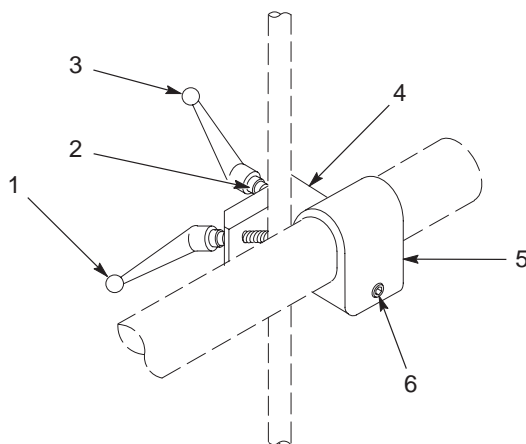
Standardmontering på holdestang af pistoler til rørmontering
